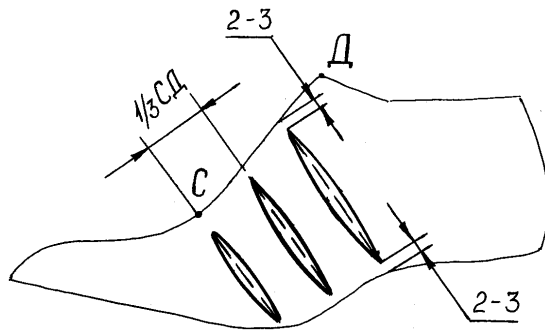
Розтин зліпку бічної поверхні колодки
